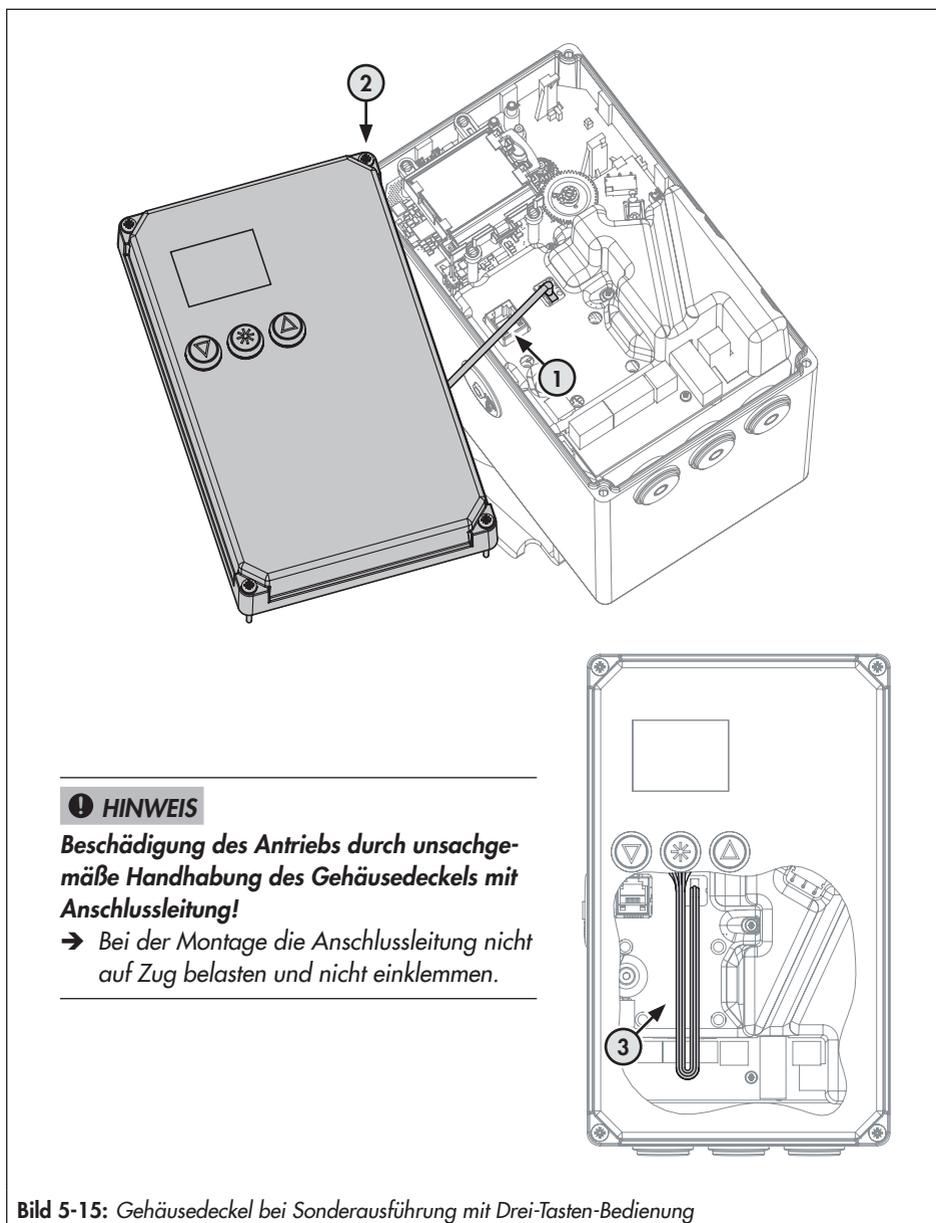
Gehäusedeckel bei Sonderausführung mit Drei-Tasten-Bedienung
